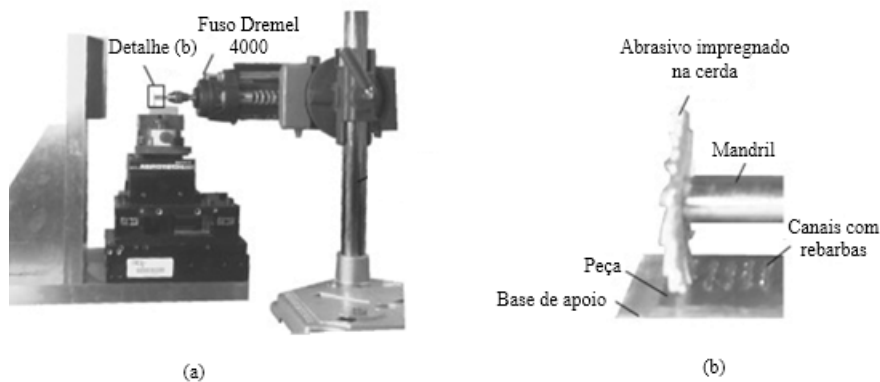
Configuração experimental: (a) Configuração para rebarbação, (b) vista detalhada da escova posicionada para rebarbação. Adaptado de (MATHAI; MELKOTE; ROSEN, 2013).
